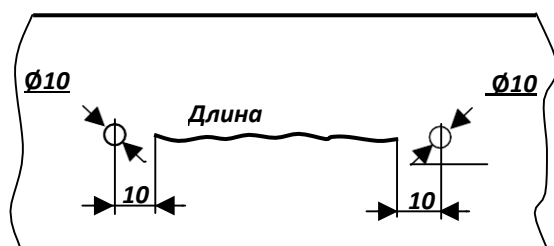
Эскиз сверловки отверстий при подготовке устранения трещины
